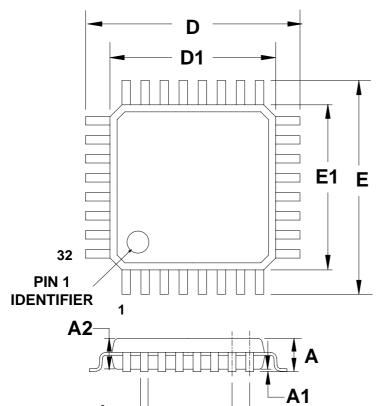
Цоколевка корпуса LQFP-32 (вид сверху)
